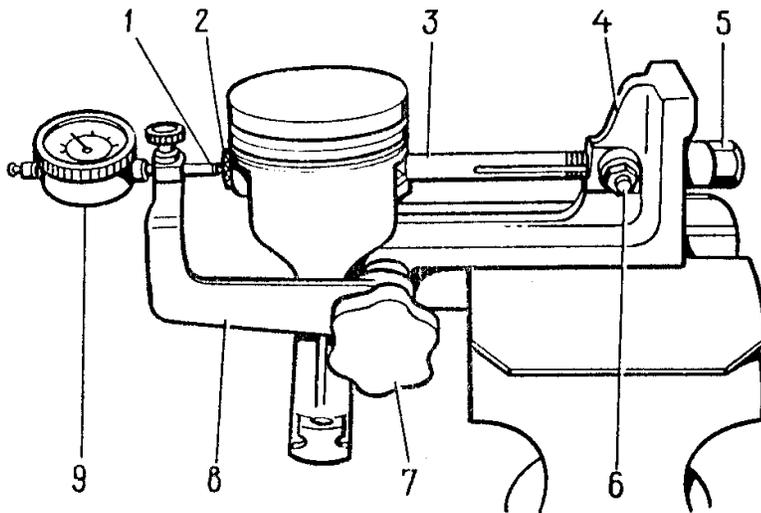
Juego pistón-bulón-biela armado e instalado en el dispositivo A.95615 para ensayar la calidad de prensado del bulón: 1 - palpador del comparador en contacto con el extremo de la varilla; 2- cabeza de la varilla en contacto con el bulón; 3- varilla roscada con ranura; 4 - base; 5 - tuerca de la varilla; 6- perno de tope de la varilla; 7-palanca para apretar el soporte; 8- soporte del comparador; 9- comparador
